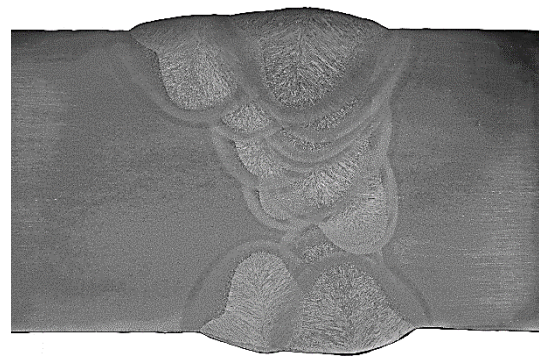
Конструктивные элементы сварного шва и технология сварки:
